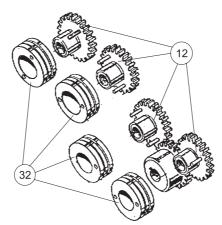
/6b. Запасные алюминиевые ролики / spare part rolls aluminium
